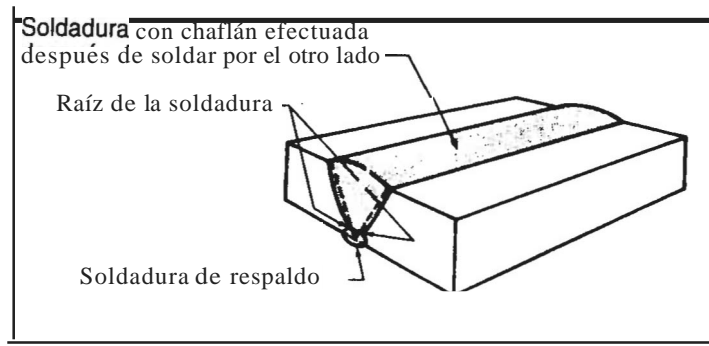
SOLDADURA DE RESPALDO
